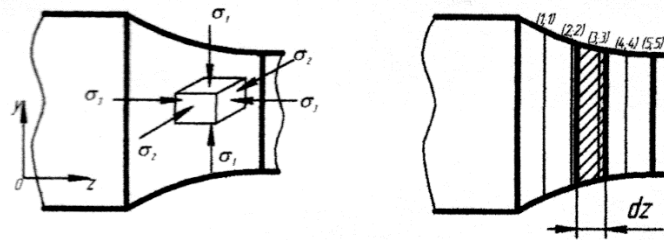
Схема напруження в перехідній зоні вальцюваної заготовки
